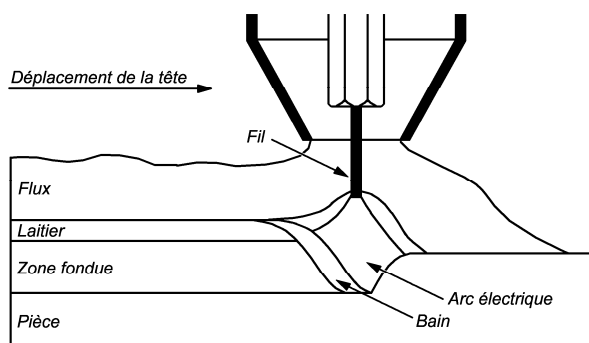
Soudage à l'arc sous flux en poudre (Institut de soudure 2021b)
